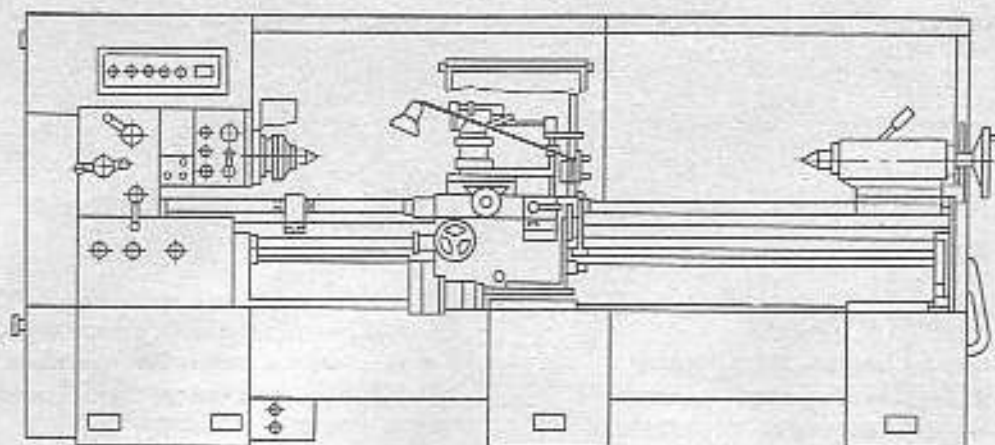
Станок токарно-винторезный I6D25 с длиной обработки  $L = 2000$  мм
